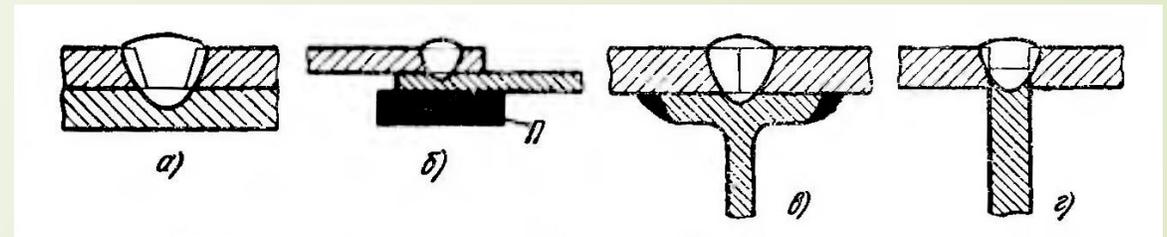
Схемы сварки электрозаклепочных и прорезных швов.
